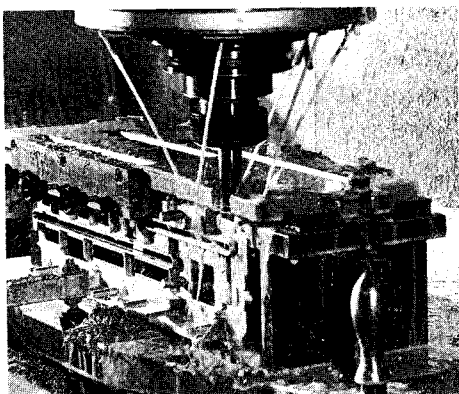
Fräsen der Schubladenführung auf einem modernen NC-Bearbeitungszenter.
